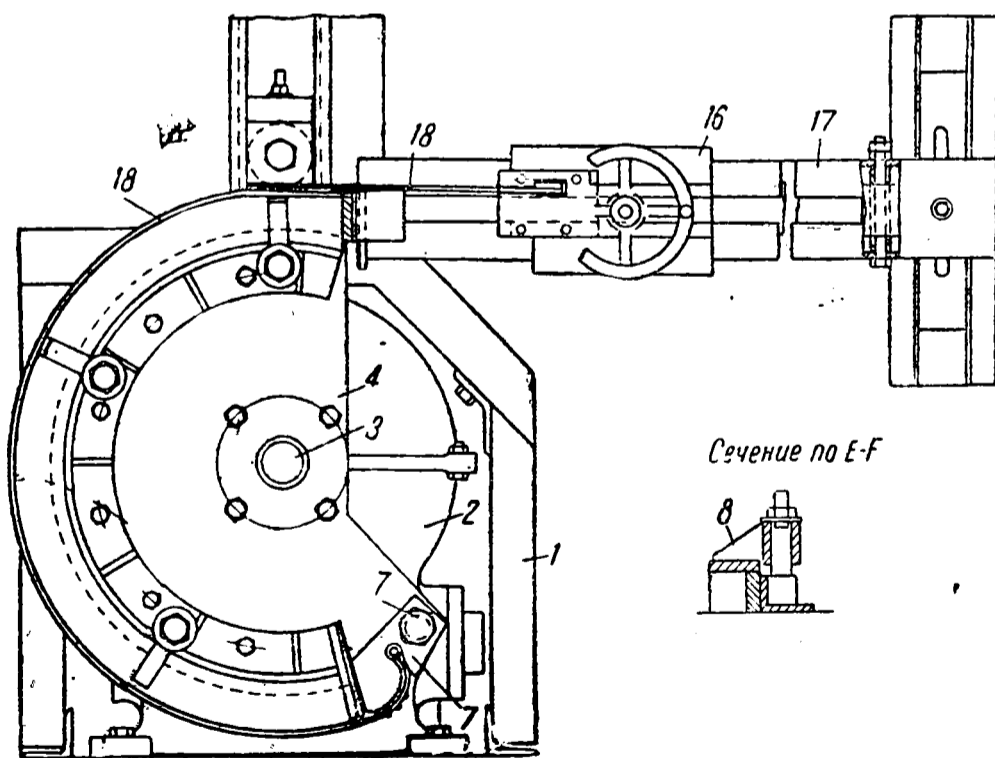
Опытный горизонтальный гнута́рный станок (разрез)
